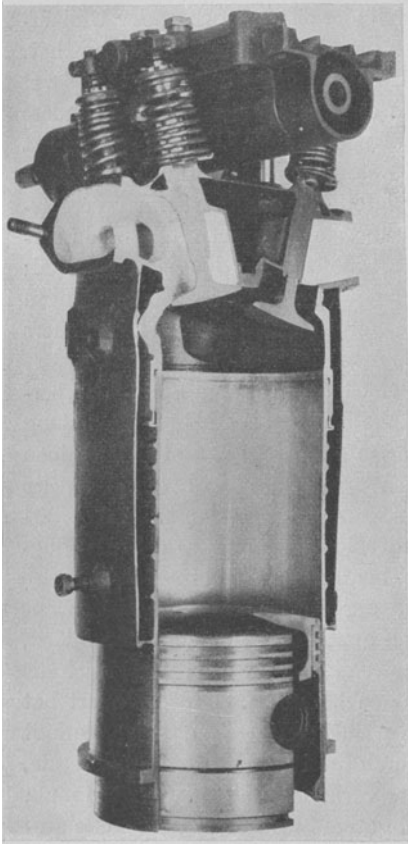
Zylinder des 260 PS-Mercedes-Flugmotors.
